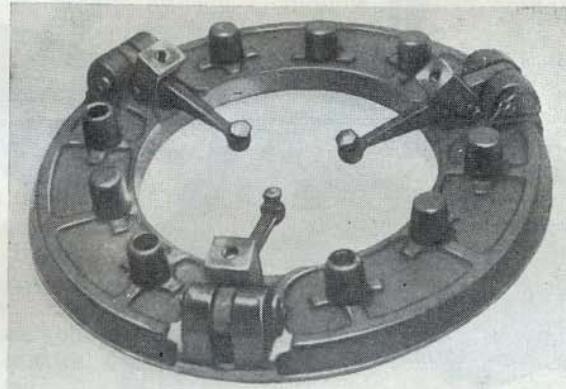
Нажимной диск с установленными рычагами выключения сцепления
